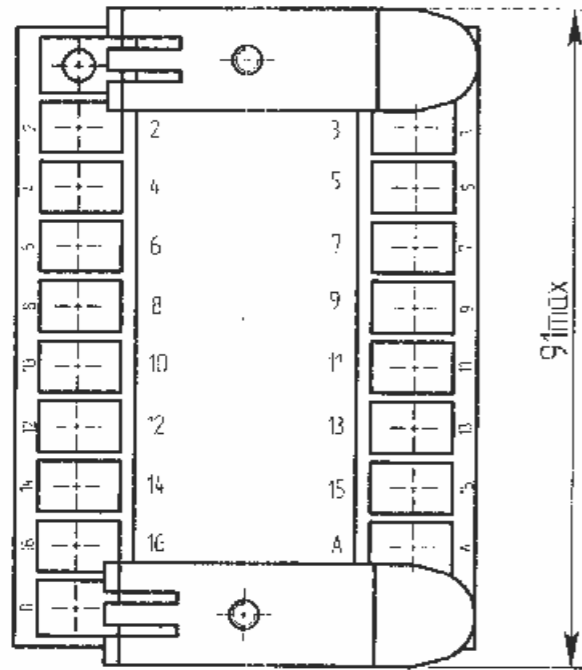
Реле типов РСВ18-11-XXXX3; РСВ19-12-XXXX3
